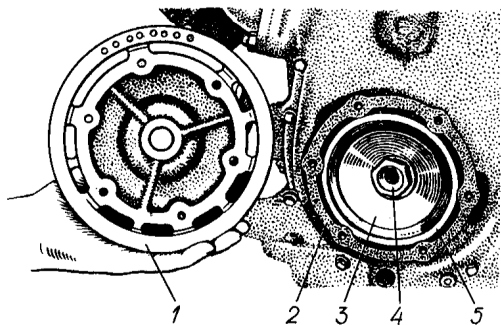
Центробежный маслоочиститель со снятой крышкой:
